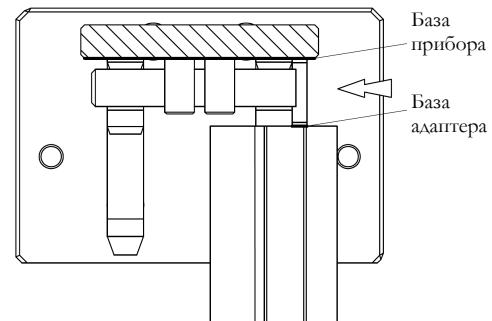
Дополнительный адаптер, вставленный в прибор 60-0253
